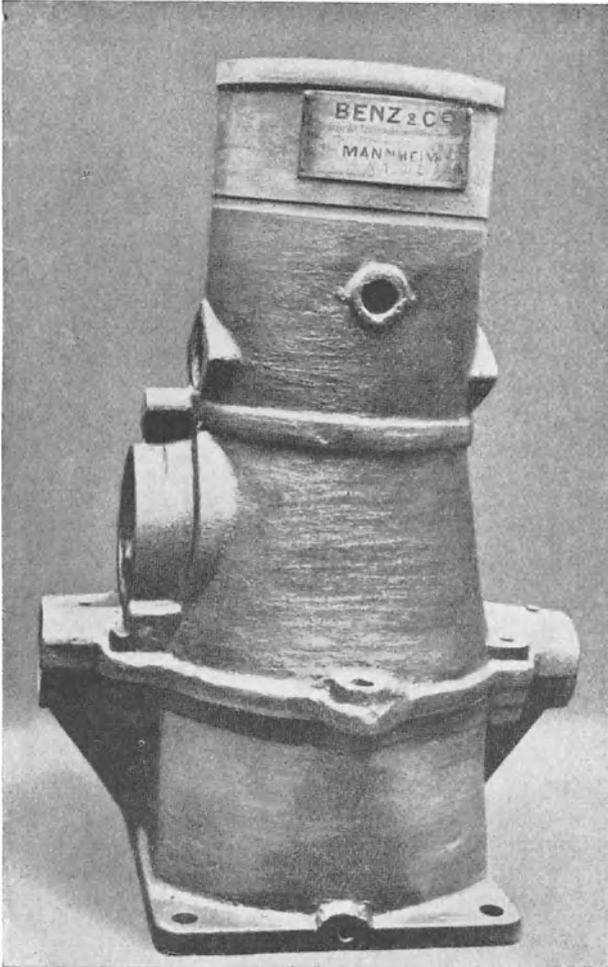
Motor der Abb. 161 nach der Schweißung.
